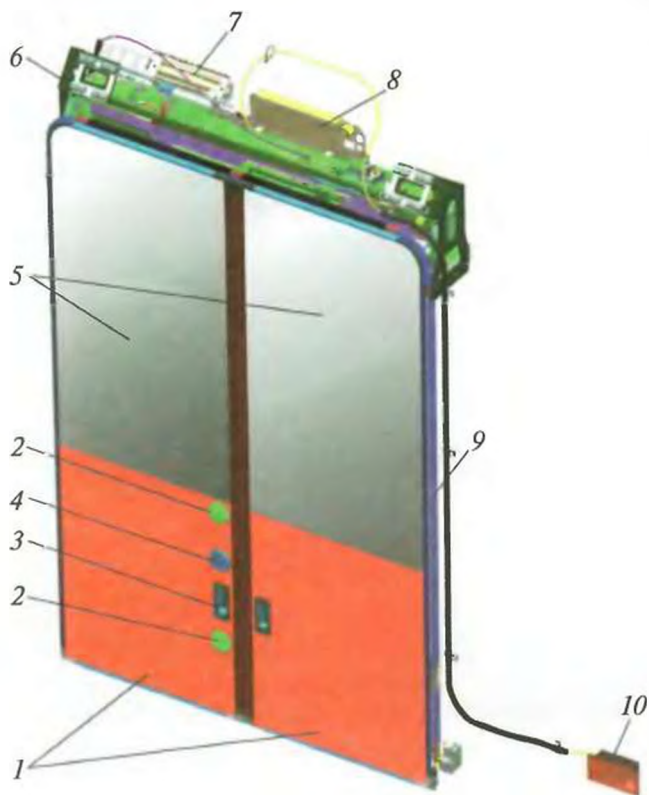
Наружная дверь вагона (вид с улицы):
